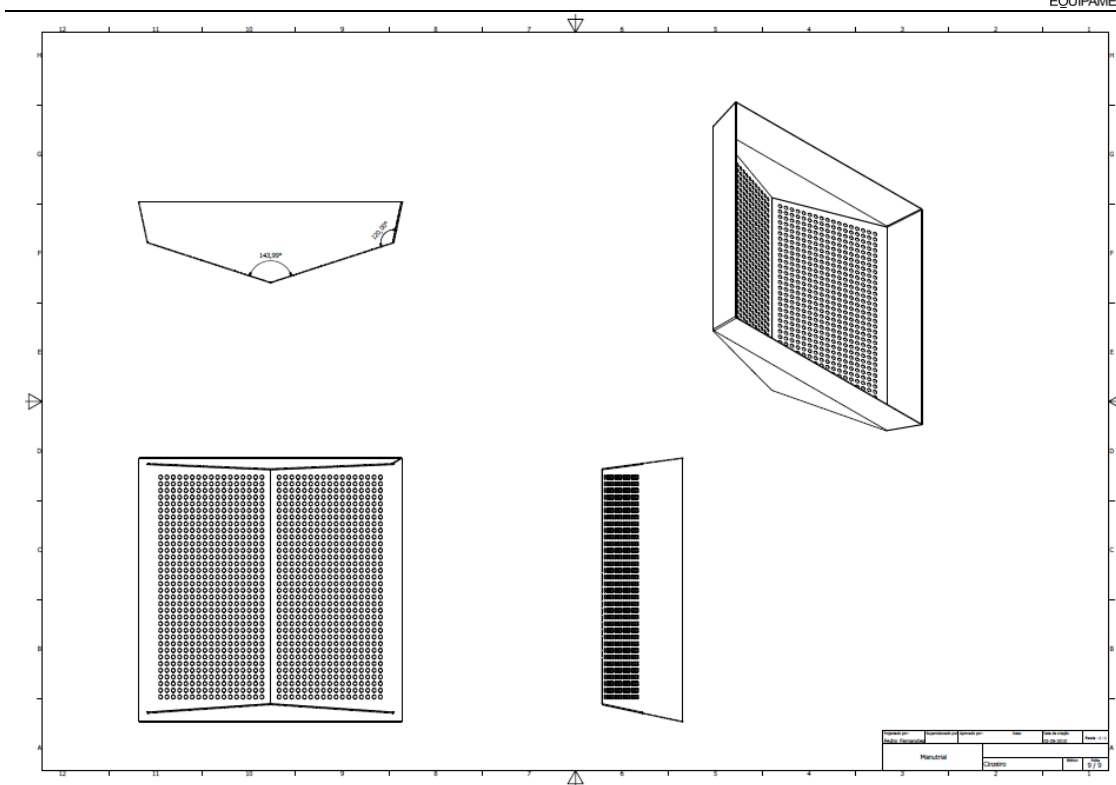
Porta beatas moldado através de quinagem da folha de chapa.
